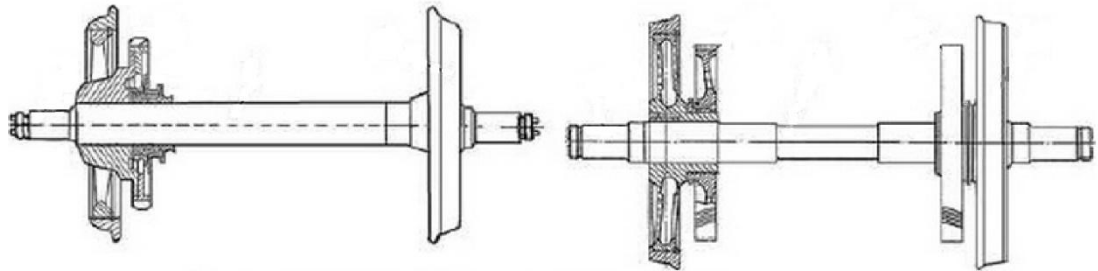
Juegos de ruedas de material rodante de tracción con posición de engranajes asimétrica y simétrica [5]
